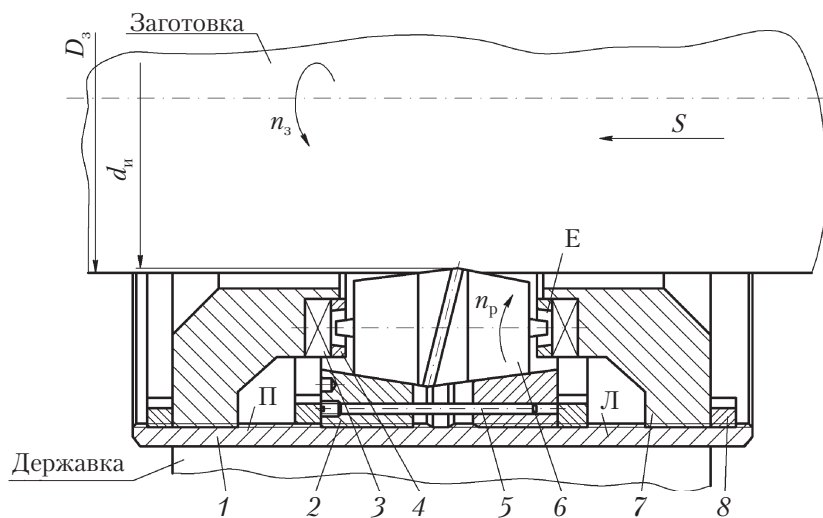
Многороликное устройство для виброобкатывания наружных цилиндрических поверхностей
